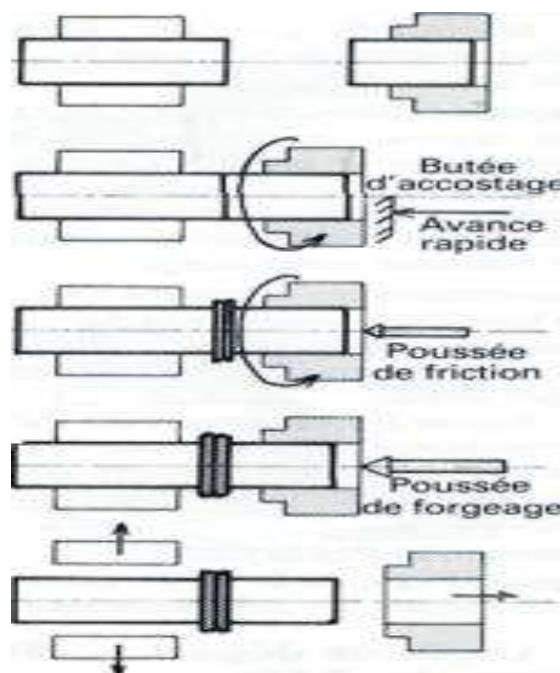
Principe de soudage par friction RFW [2].
